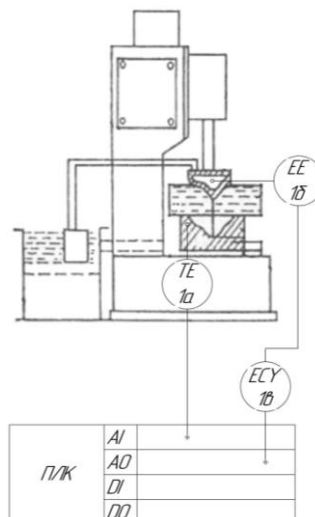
Контур регулювання процесу електроерозії заготовки електродом-інструментом
